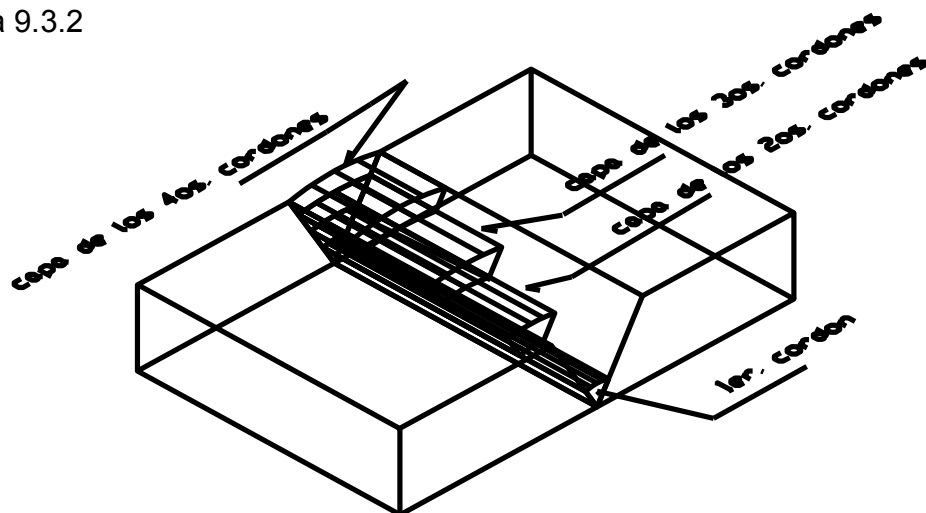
Muestra de cómo fue aplicada la soldadura en multipaso.
